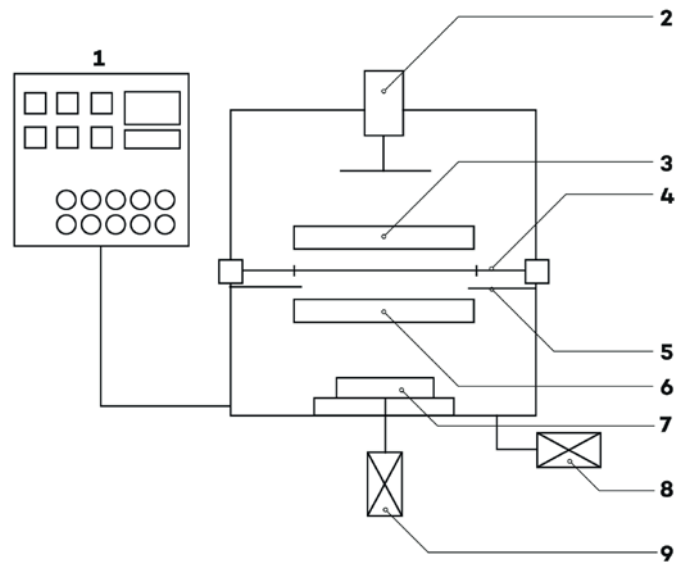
Schema einer Tiefziehmaschine: Steuerschrank (1), Oberstempel (2), Oberheizung (3), Spannrahmen (4), Fensterplatte (5), Unterheizung (6), Werkzeuggestisch mit Formwerkzeug (7), Druckluft (8), Vakuum (9)
